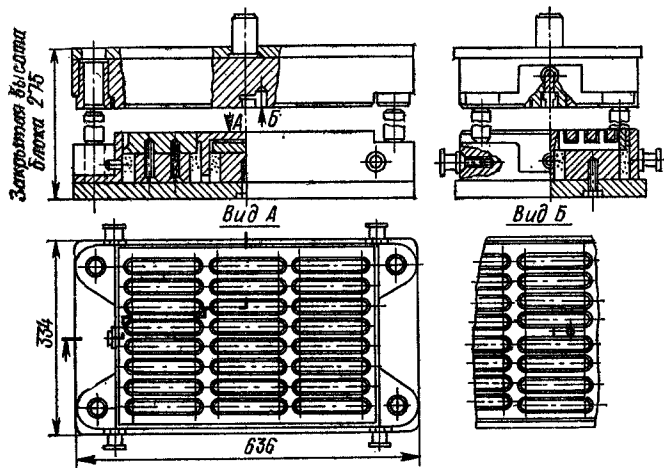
Электромагнитный блок для крепления пластинчатых штампов
